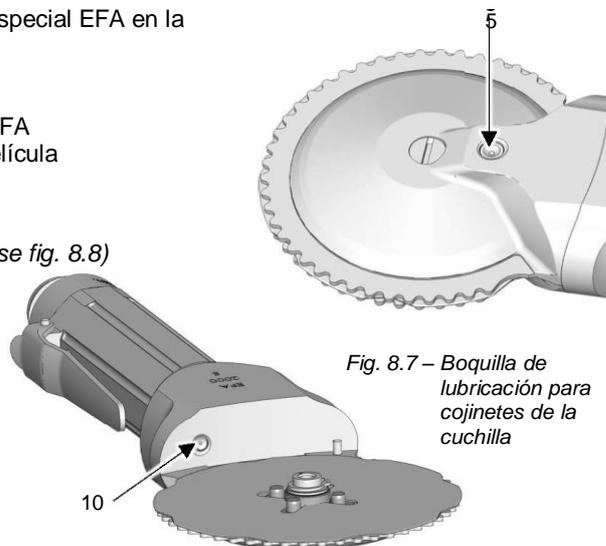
Boquilla de lubricación para cojinetes de la cuchilla
